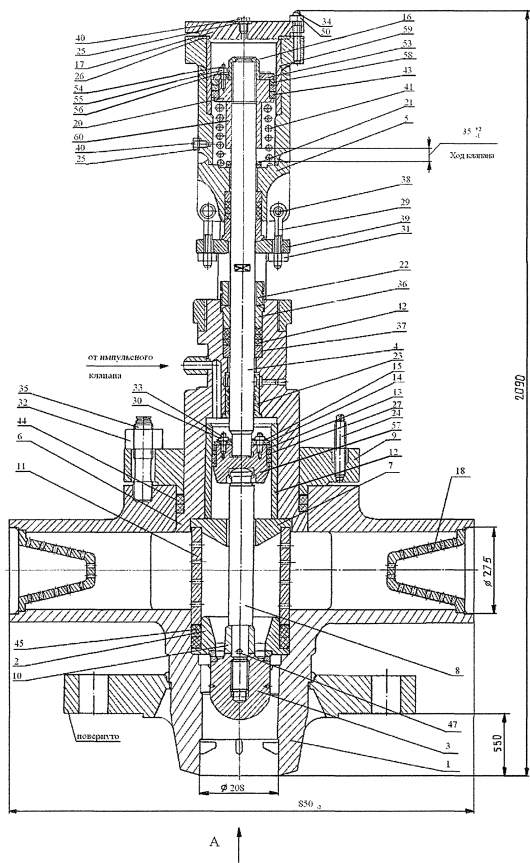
Клапан главный предохранительный 1029-200/250-0
